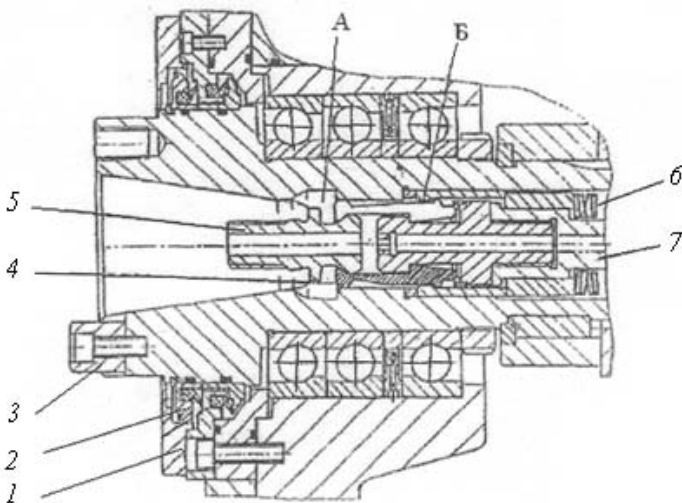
Шпиндельный узел многоцелевого фрезерно-сверлильно-расточного станка
